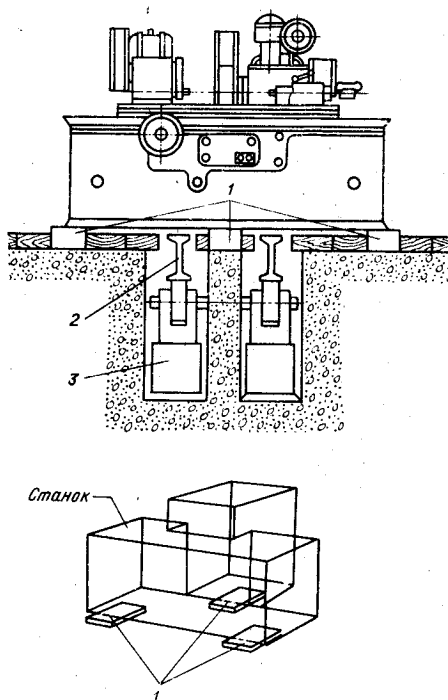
Схема шагающего рамного конвейера для сборки станков
